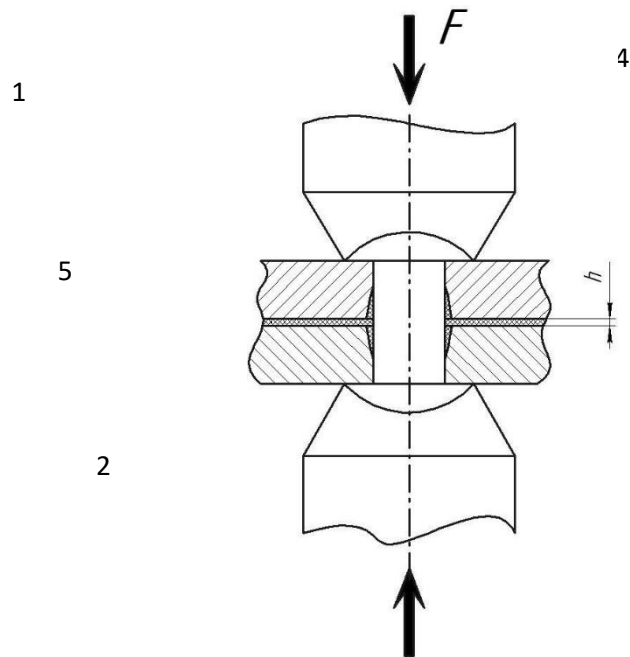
Схема отримання клеєклепаного з'єднання: 1, 2 - з'єднуються деталі; 3 - заклепка; 4 - інструмент для установки заклепок; 5 - клейовий шов товщиною h
